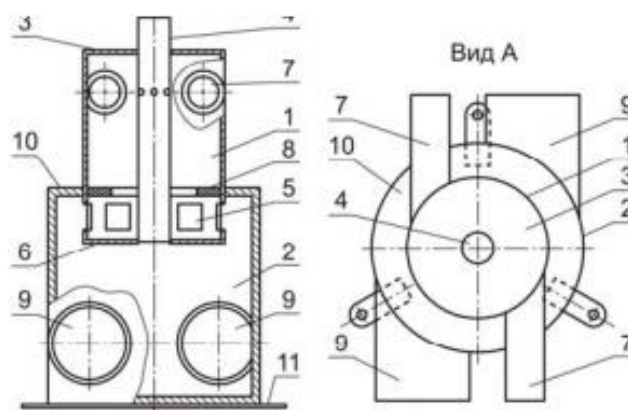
Конструктивная схема деаэратора ДЦВ-670: 1 – корпус; 2 – центробежный сепаратор; 3, 6 – верхняя и нижняя торцевые крышки корпуса соответственно; 4 – трубопровод отвода пара; 5 – окна для отвода воды из корпуса; 7, 9 – подводящие и отводящие тангенциальные патрубки соответственно; 8 – кольцевая перегородка (шайба); 10, 11 – верхняя и нижняя торцевые крышки центробежного сепаратора соответственно
